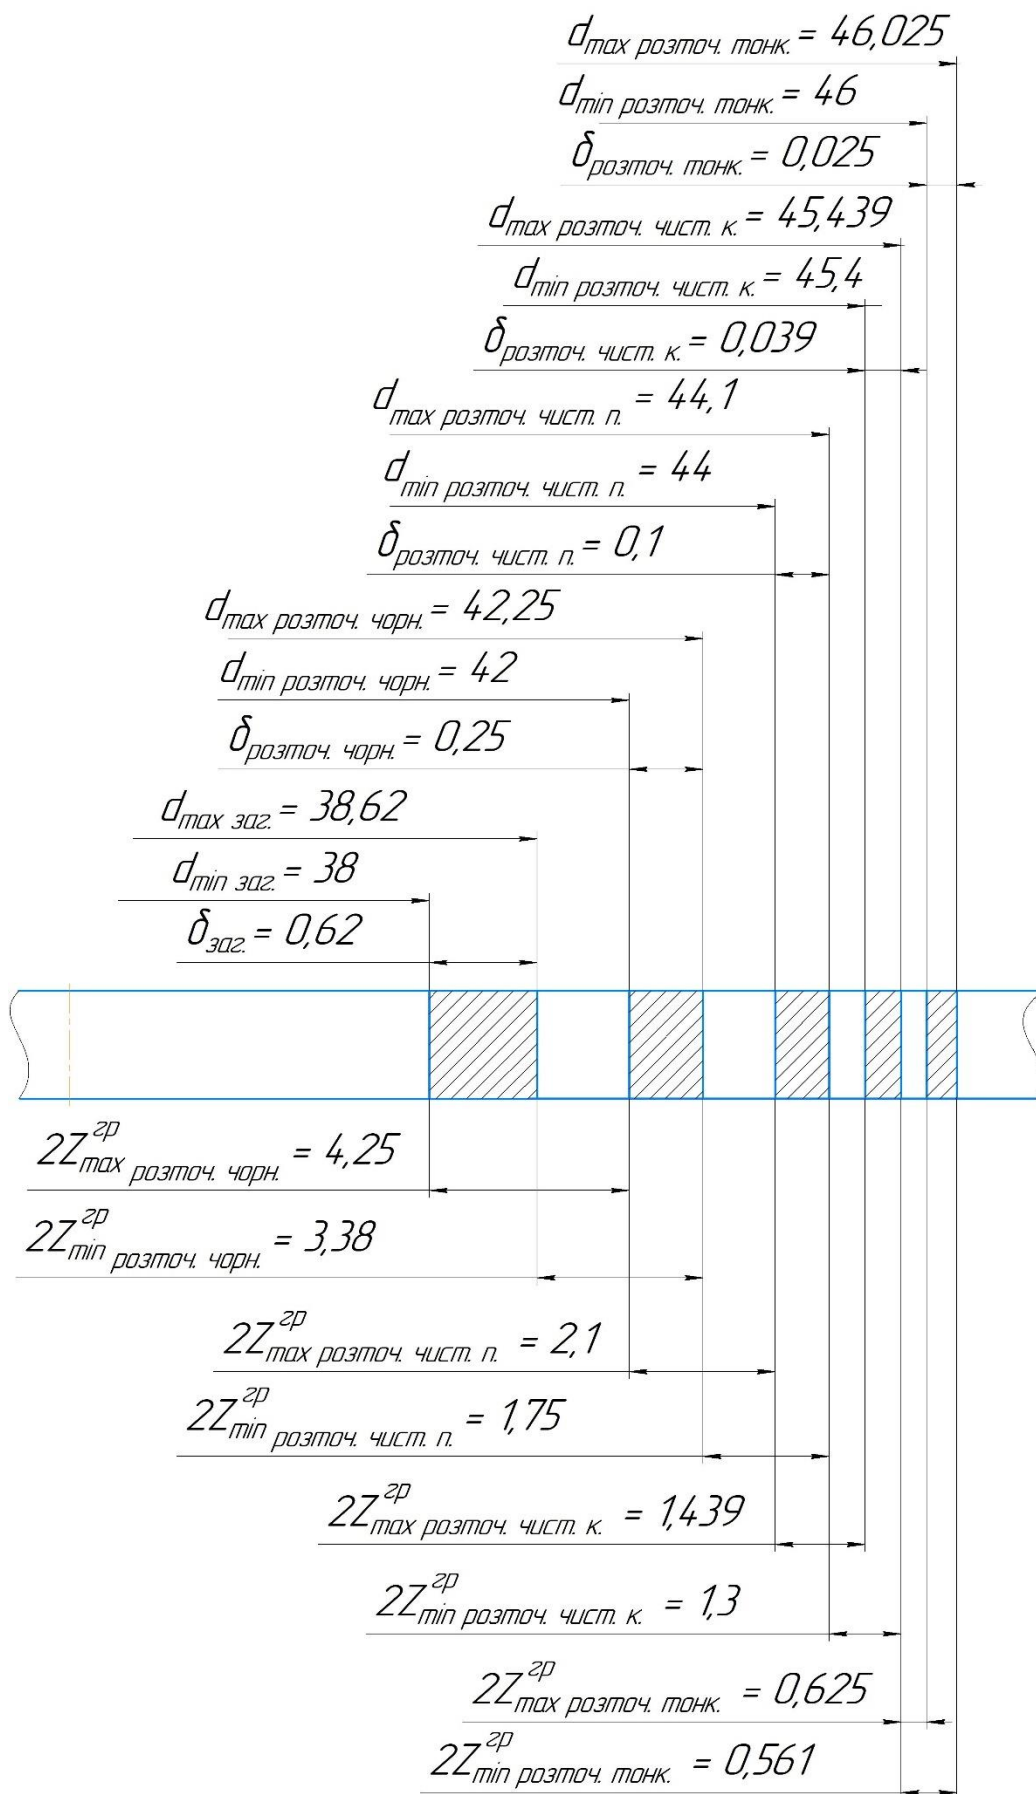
Схема графічного розташування припусків і допусків для внутрішньої циліндричної поверхні $\varnothing 46^{+0,025}$
